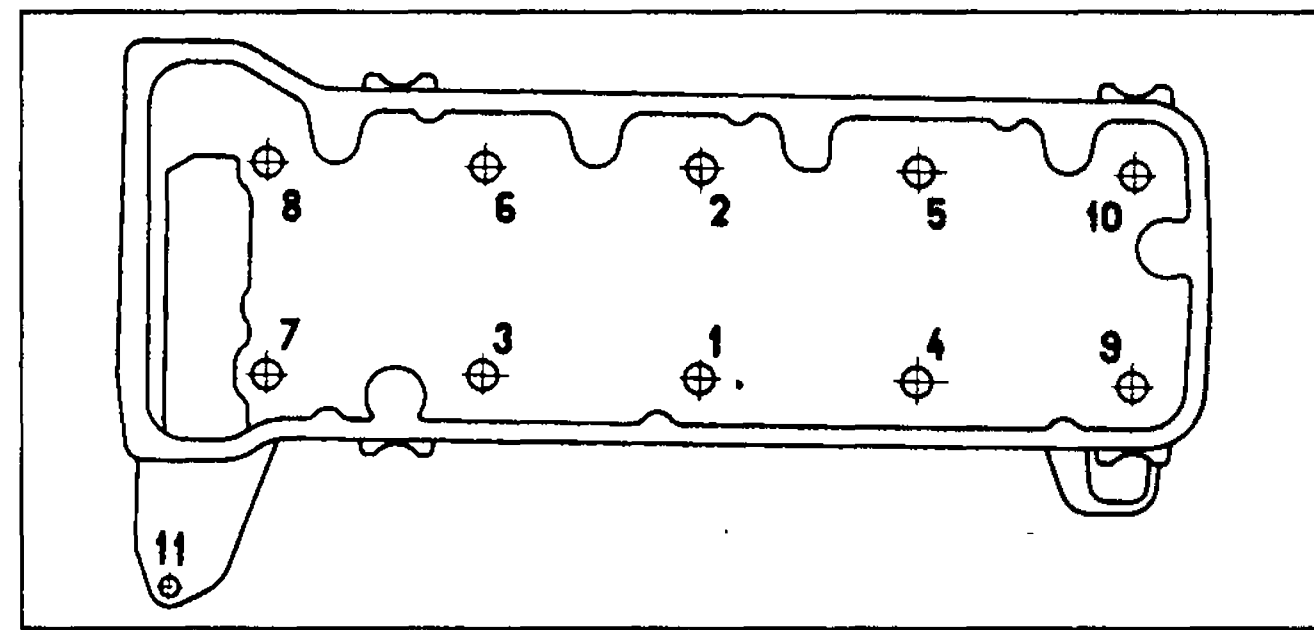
Порядок затягивания болтов головки блока цилиндров
